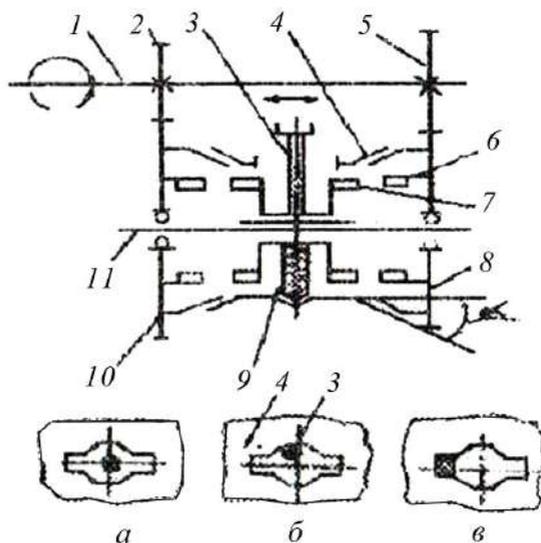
Принципова схема інерційного синхронізатора
